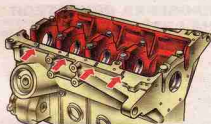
Маркировка размерного класса цилиндров на блоке
